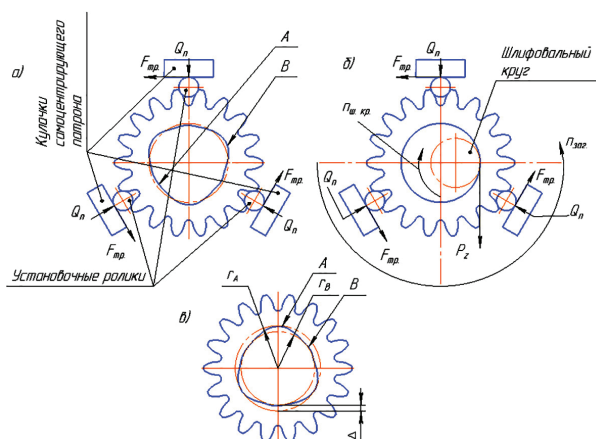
Схема нагружения и возникновения погрешности формы отверстия заготовки зубчатого колеса: а) упругая деформация заготовки при закреплении в трехкулачковом патроне; б) форма отверстия после шлифования; в) форма контура отверстия после раскрепления заготовки
